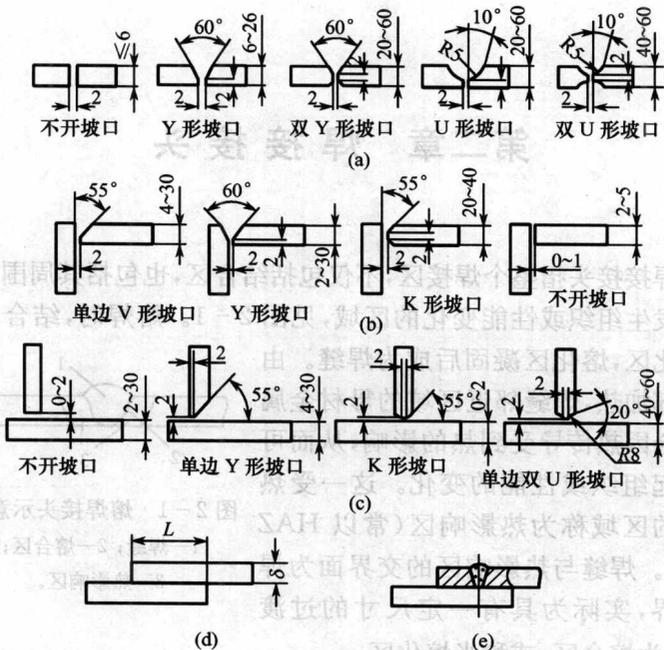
焊条电弧焊常用接头形式和坡口形式
